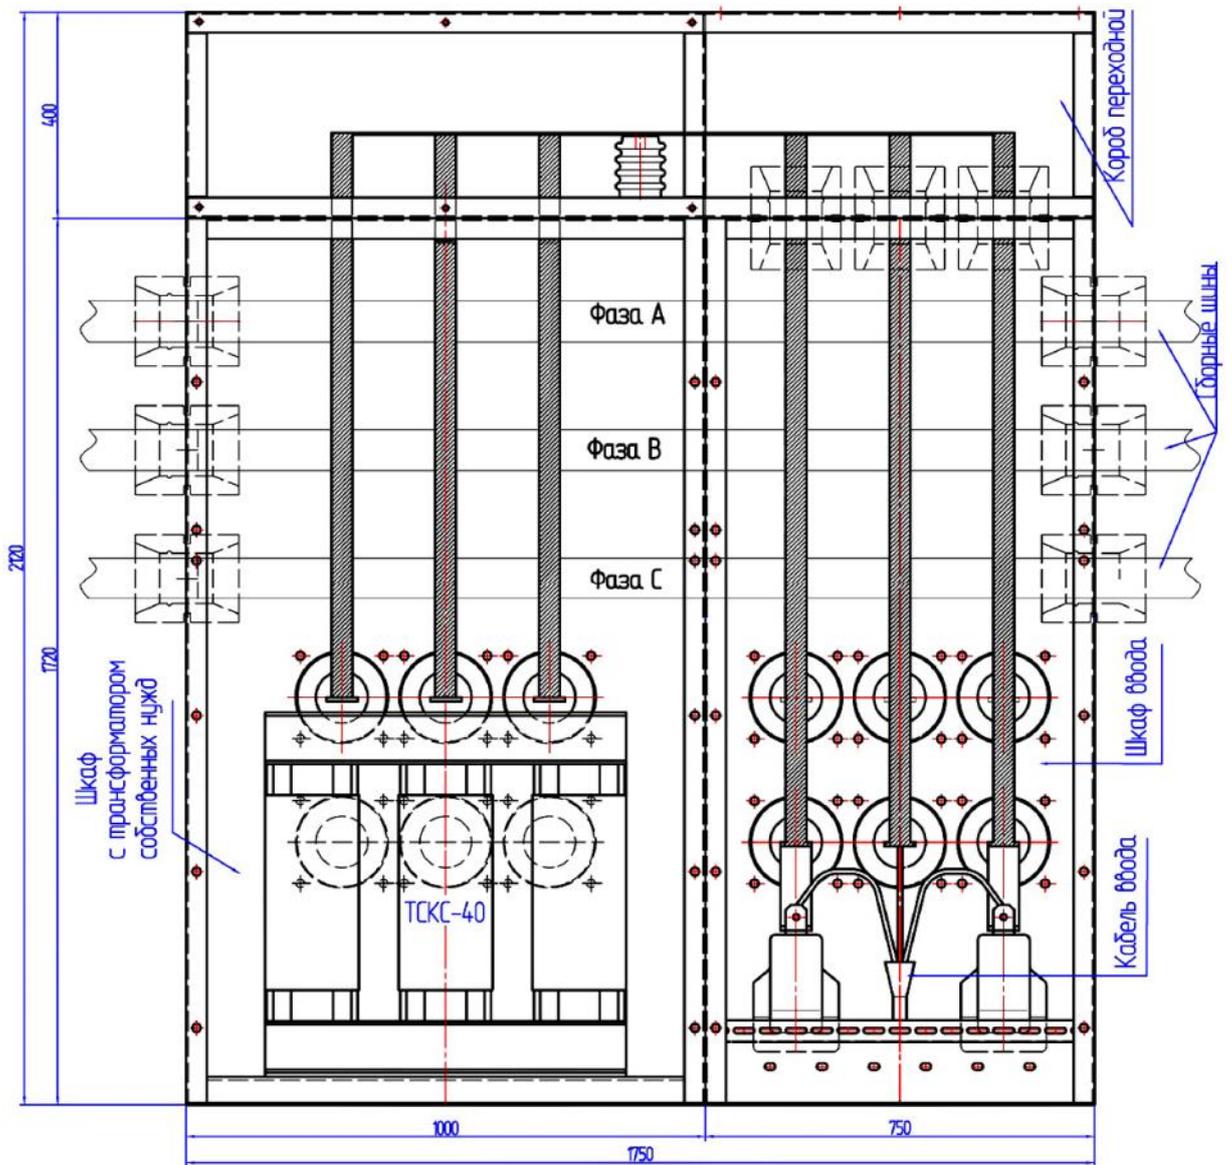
Шкаф КМ-1КФ - вид сзади на шины присоединения
